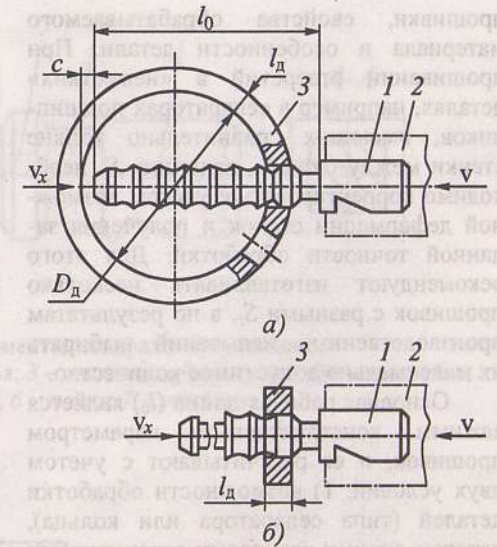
Схемы работы прошивки при обработке окон сепаратора подшипников (а) и втулки (б):
